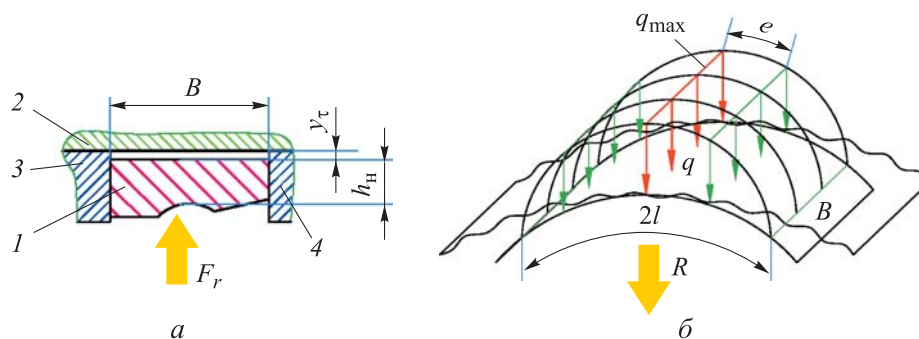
Расчетные схемы подшипника (1 — наружное кольцо подшипника; 2 — корпус ШУ; 3 — втулка; 4 — крышка) (а) и нормального контакта цилиндрических тел (б)
